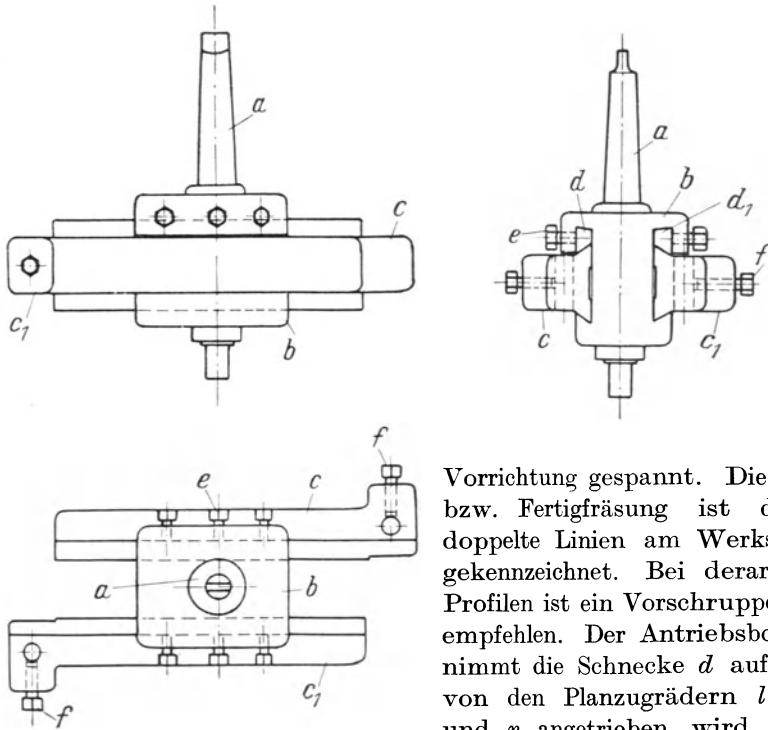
Fräsvorrichtung für starke Blechplatten.
